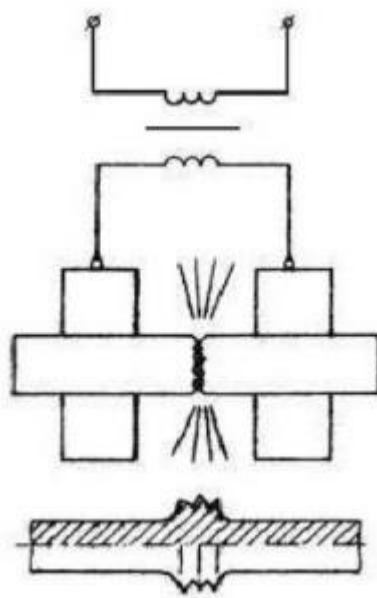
Схема контактно стыковой сварки оплавлением
